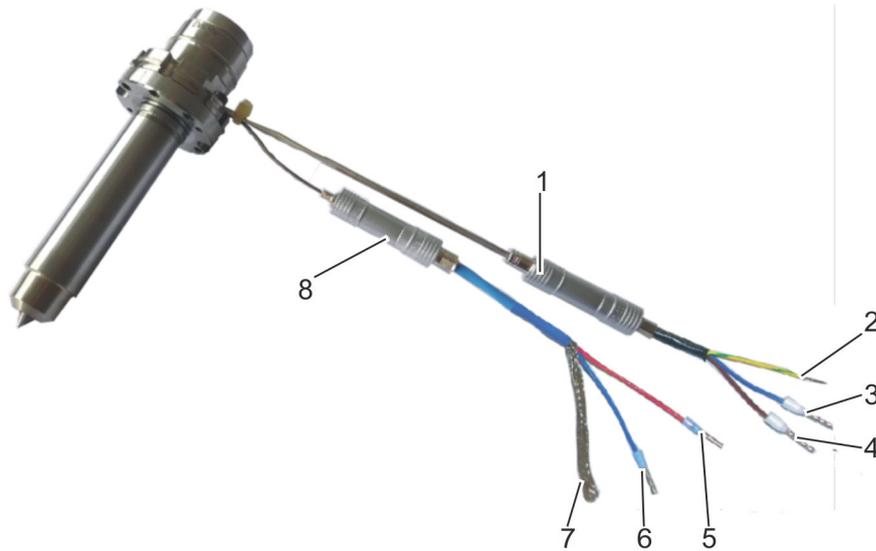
Vue d'ensemble de la buse à canal chaud FKT
